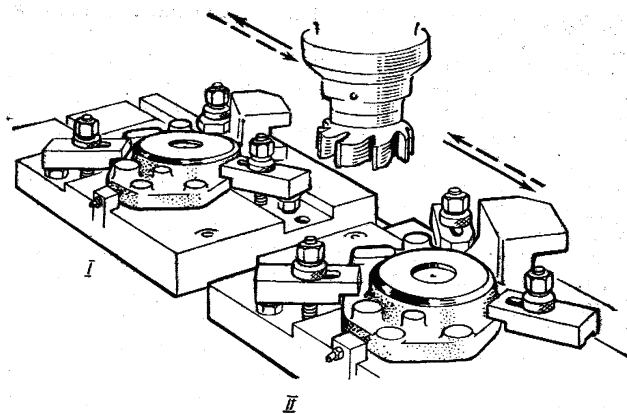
Обробка заготовок корпусних деталей по схемі маятникового фрезерування
